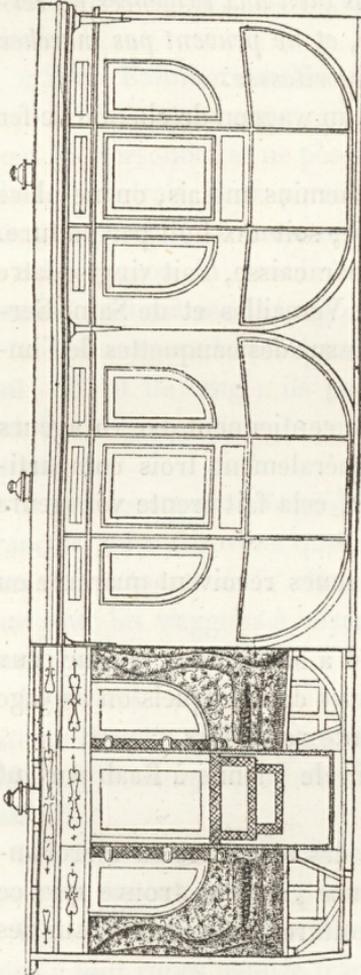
Élévation et coupe d'une voiture de 1^{re} classe.
